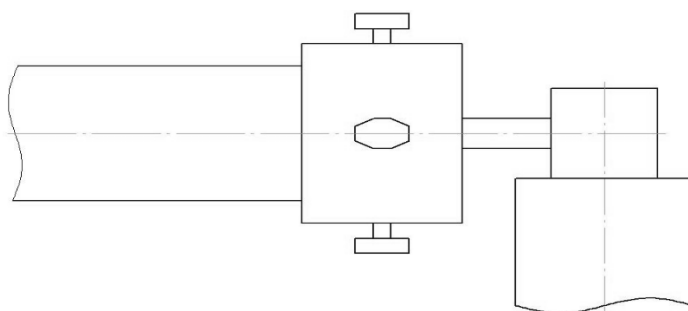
Процесс установки первого образца в сборочное приспособление
